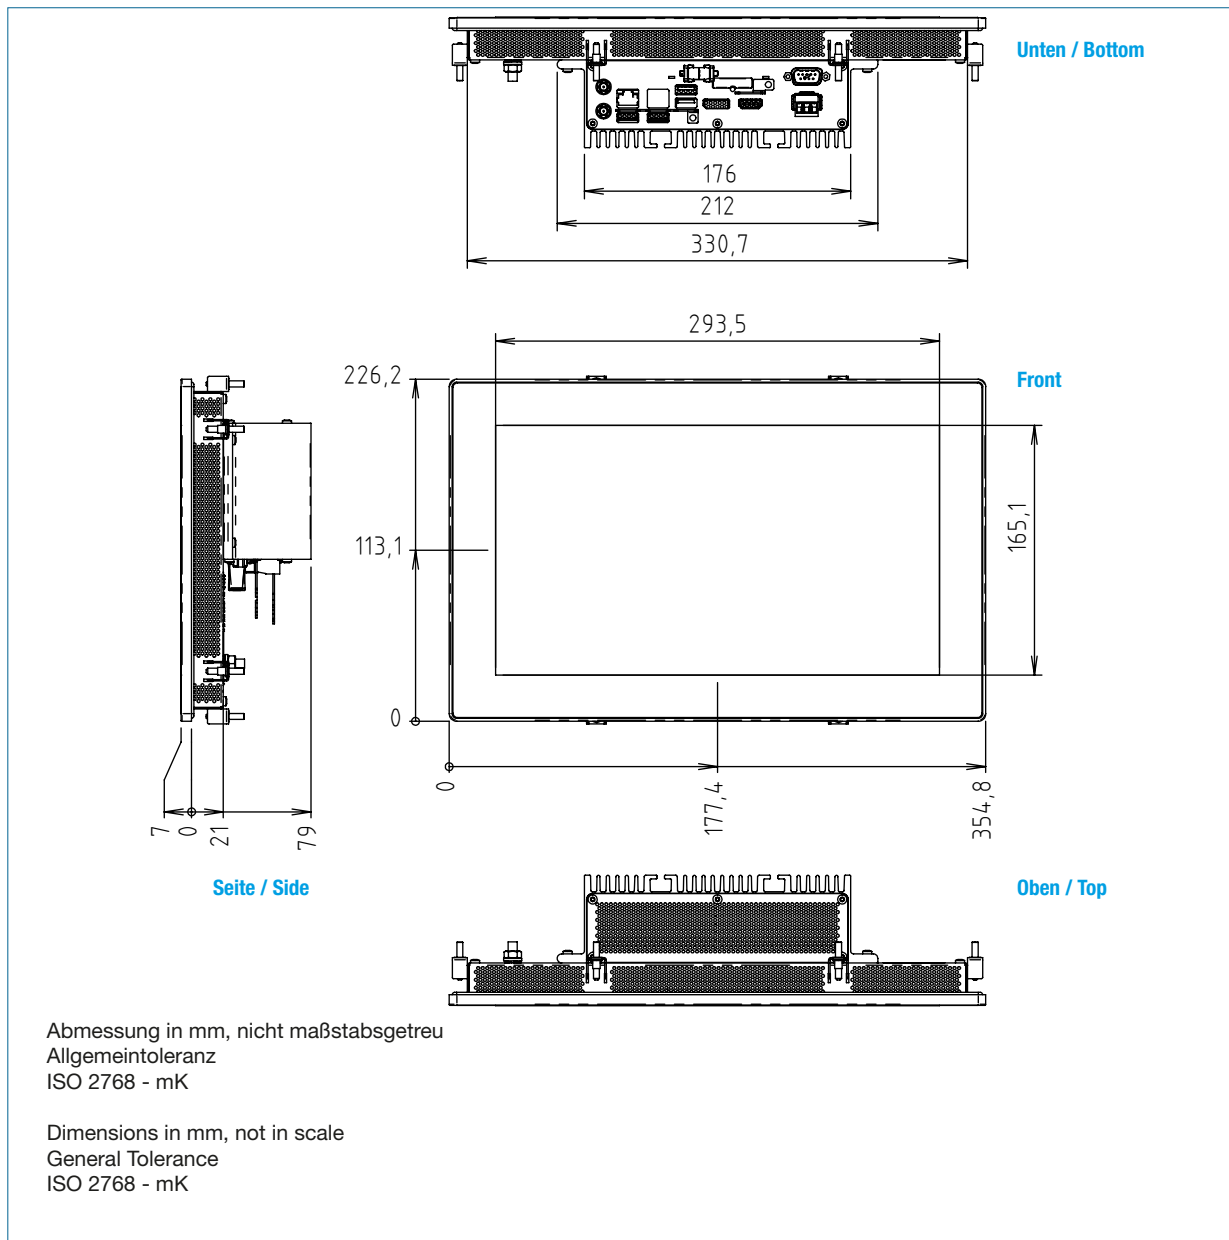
13,3" Prime Panel Pico Einbau - Gerätemaße
